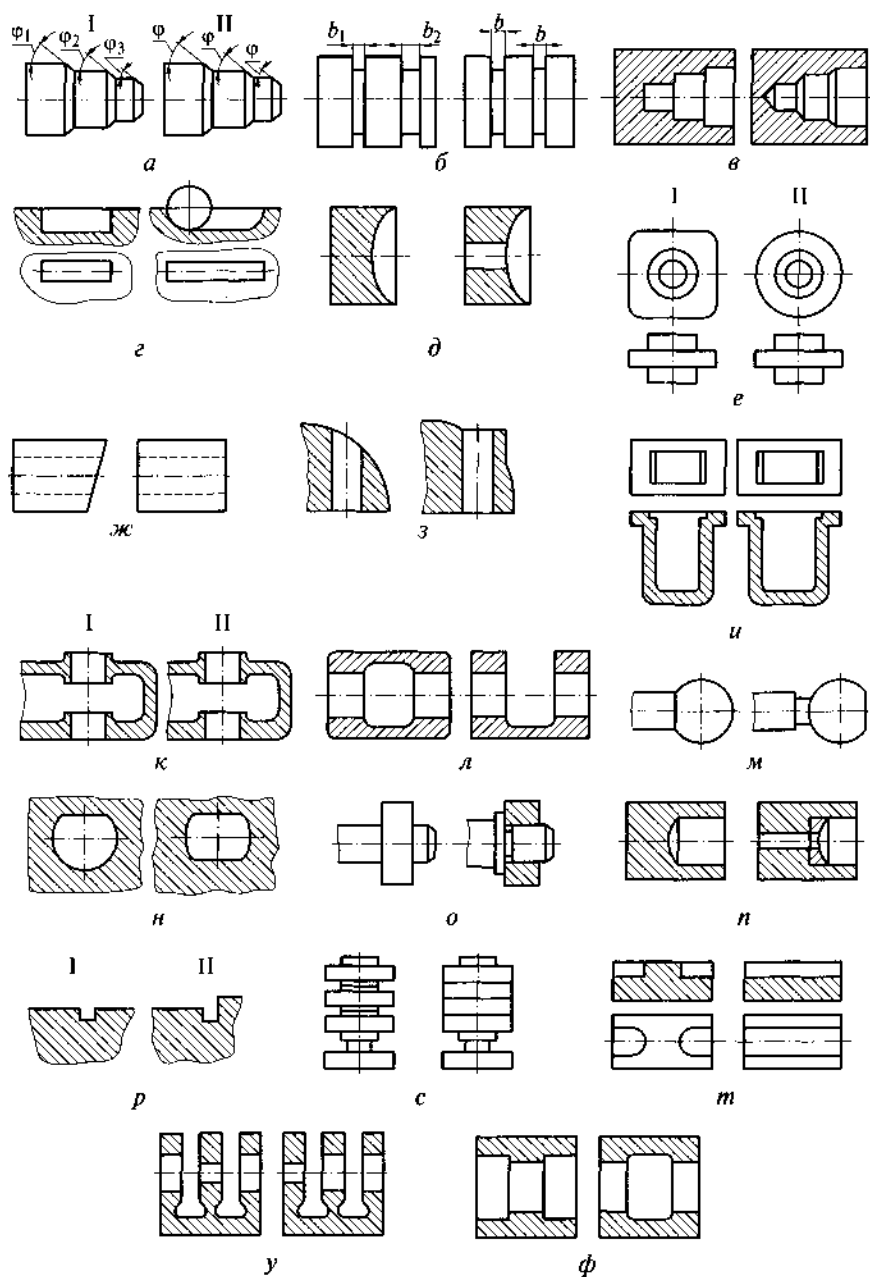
Детали, обрабатываемые на металлорежущих станках:
